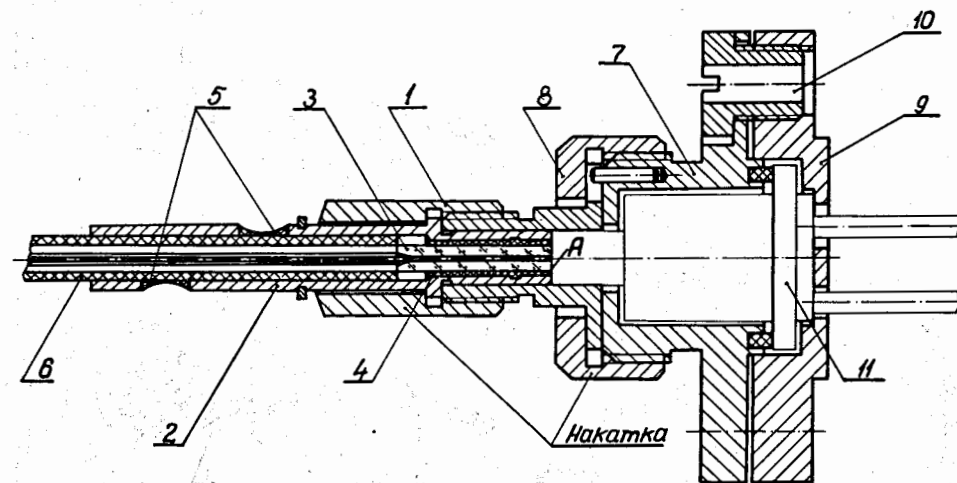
Универсальный юстируемый разъемный соединитель: (1 — накидная гайка; 2 — хвостовик; 3 — капилляр; 4-5 — эпоксидный компаунд; 6 — оболочка ВОК; 7 — корпус приборный; 8 — фиксатор; 9 — основание приборной части ОС; 10 — элемент крепления; 11 — суперлюминисцентный светодиод ИПЛН-301).
